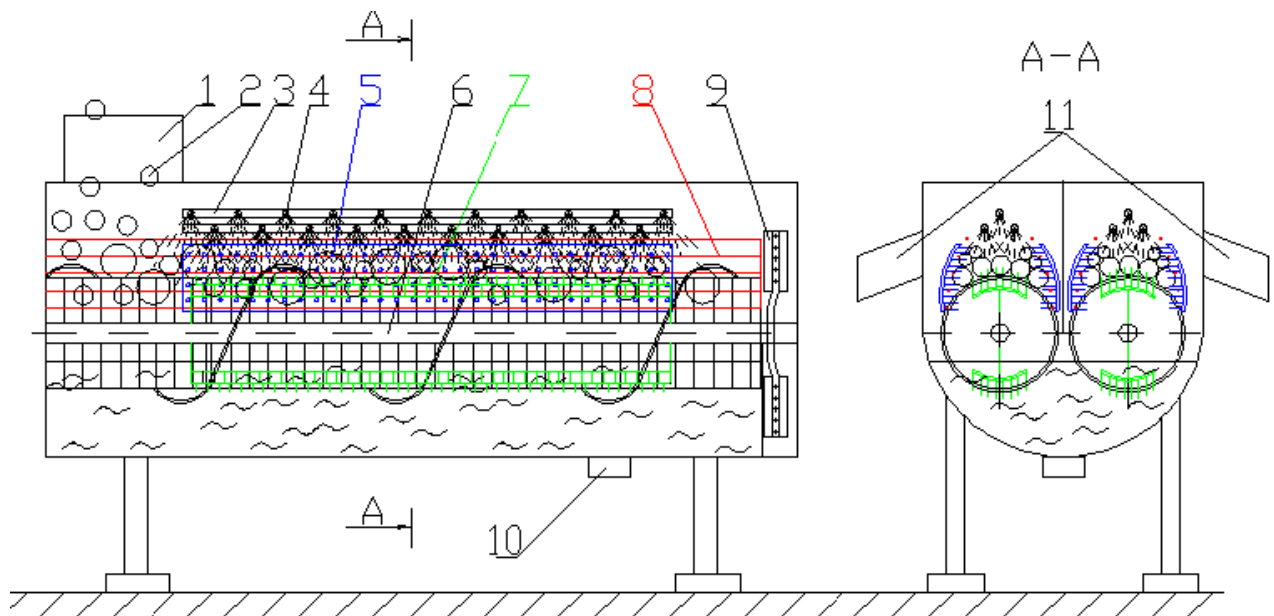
Схема шнеково-щіткової машини: 1 – завантажувальний лоток; 2 – коренебульбоплоди; 3 – душовий колектор; 4 – форсунка; 5 – щітка (вібруюча); 6 – барабан; 7 – щітка; 8 – прутковий кожух; 9 – вивантажувальний механізм; 10 – зливний люк; 11 – вивантажувальні горловини
